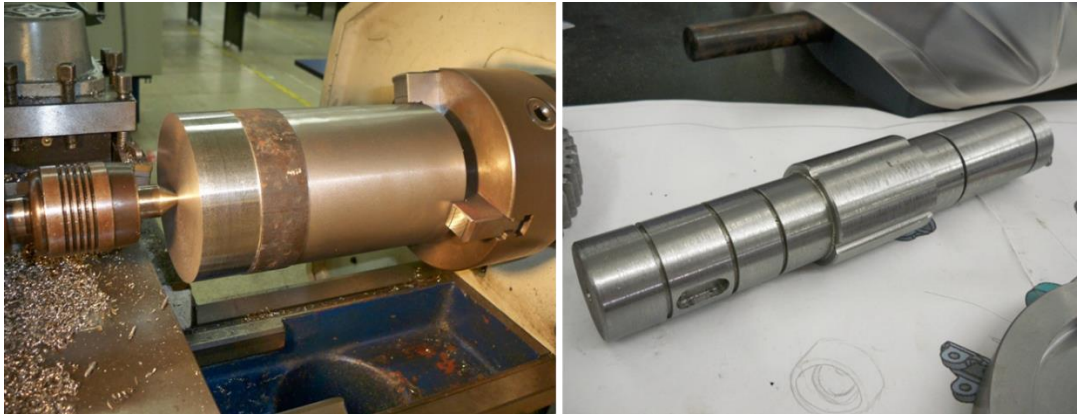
Resultado del maquinado de los engranajes de la caja de cambios
